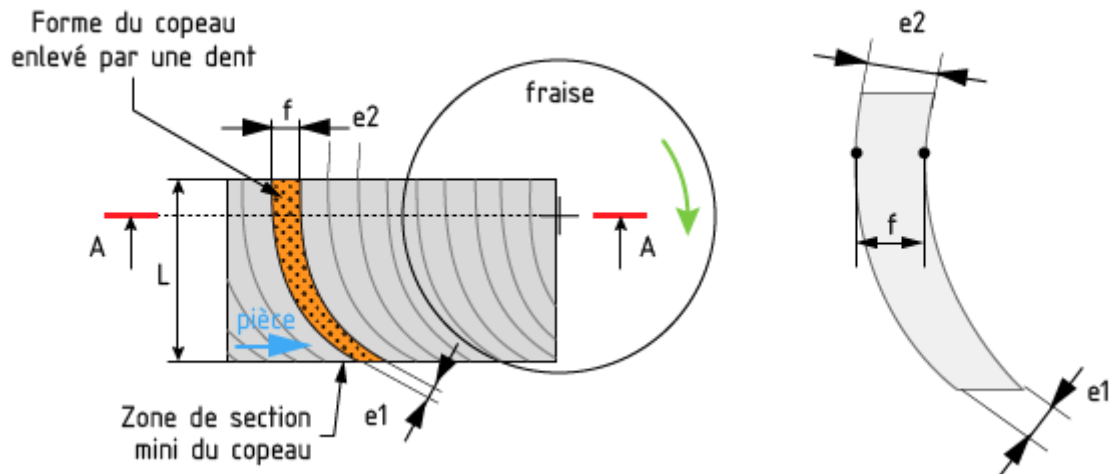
La forme du copeau enlevé par une dent pour le fraisage en bout
